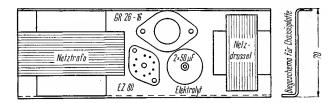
Aufbauschema für das Chassis des Universal-Netzgerätes
